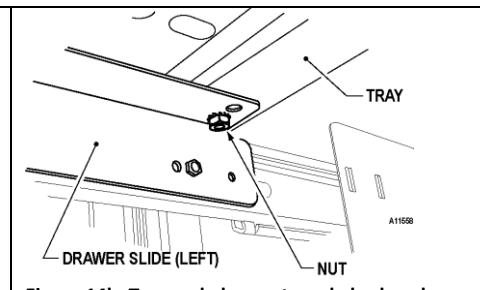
Tuerca de la montura de la charola – parte trasera izquierda
